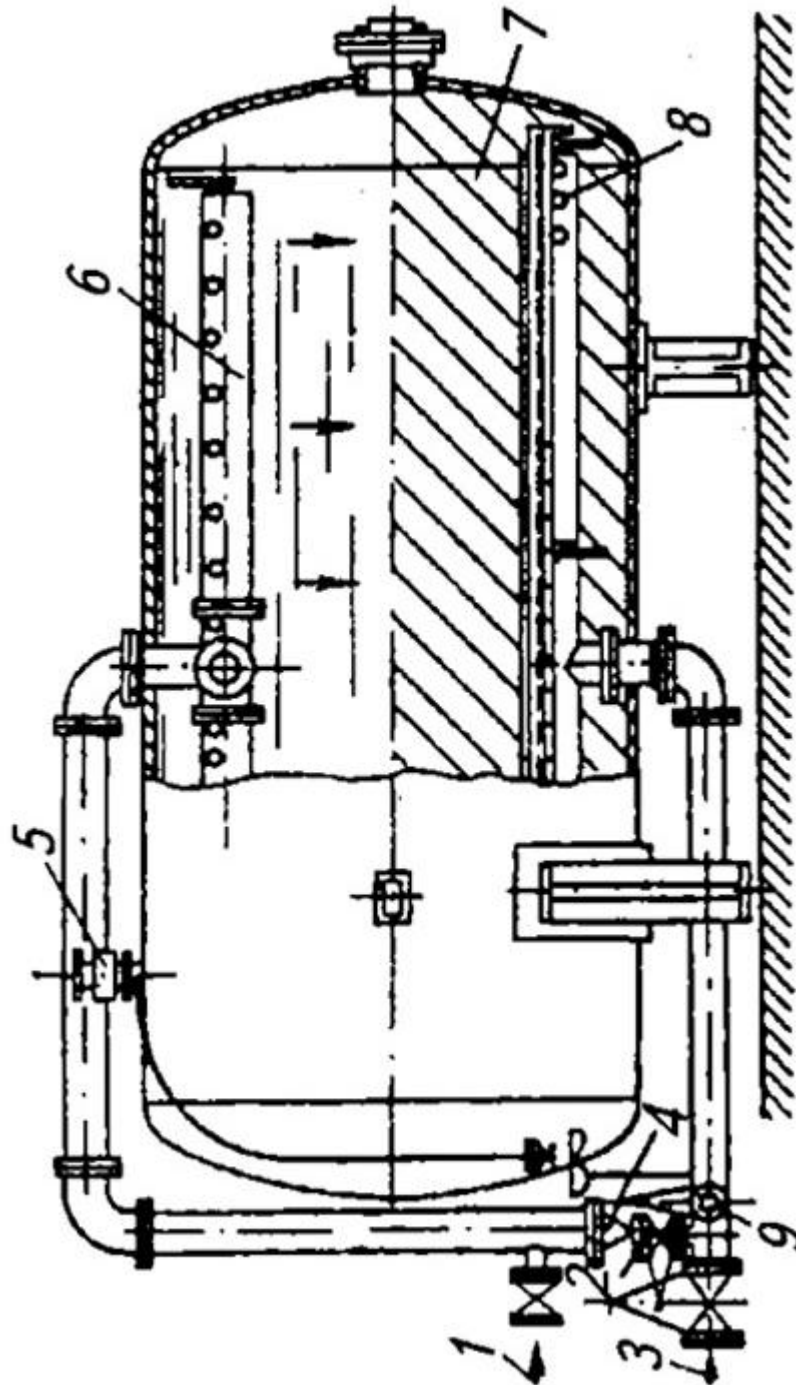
Фильтр механический горизонтальный однокамерный
